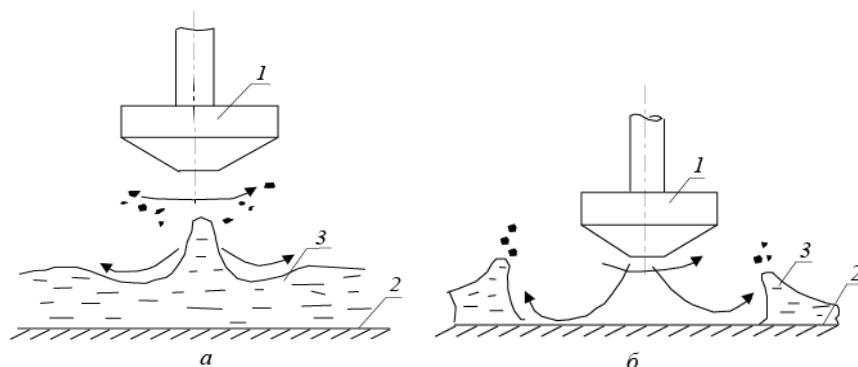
Раздувка шлакового расплава вихревыми газовыми струями:
